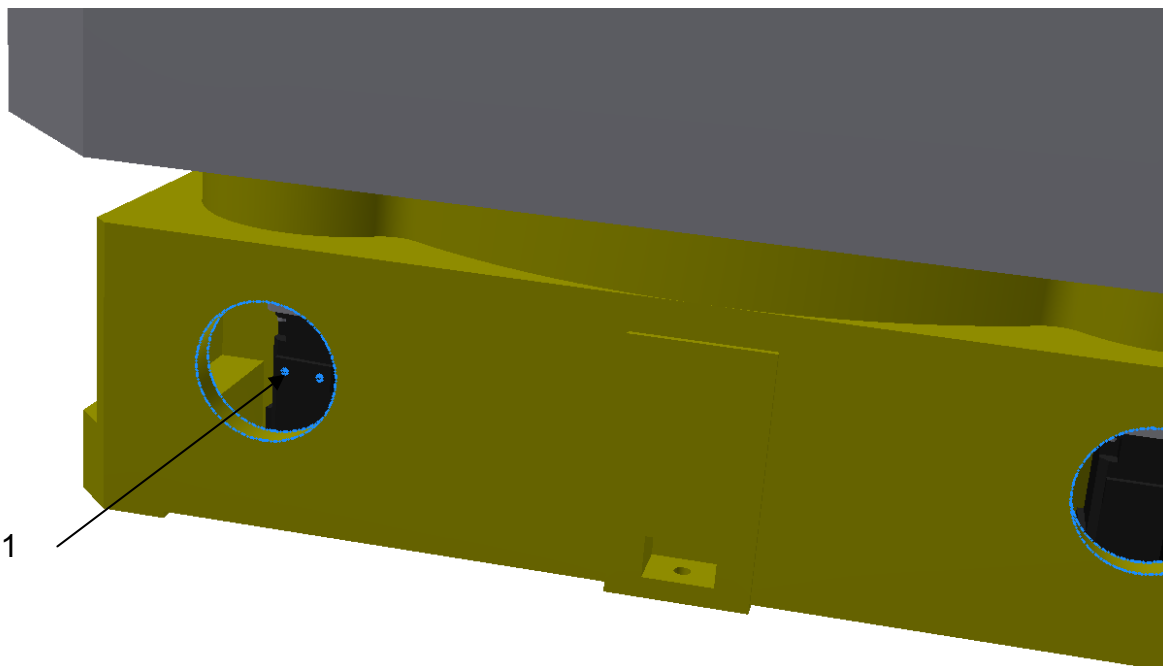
Uložení pohonu na desce motoru připevněné k rámu
